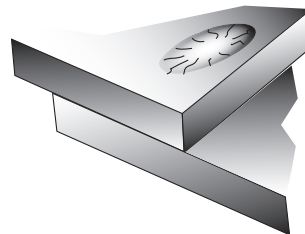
Joint typique pour le soudage à l'arc
